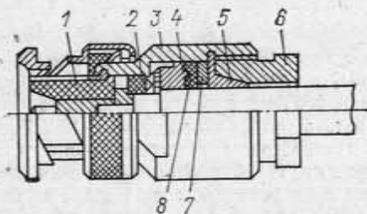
Соединитель радиочастотный в сборе с разделанным кабелем. 1 — изолятор; 2 — изолирующая шайба; 3 — корпус соединителя; 4 — шайба; 5 — сухари; 6 — зажимная втулка; 7 — шайба; 8 — уплотнительное кольцо.
